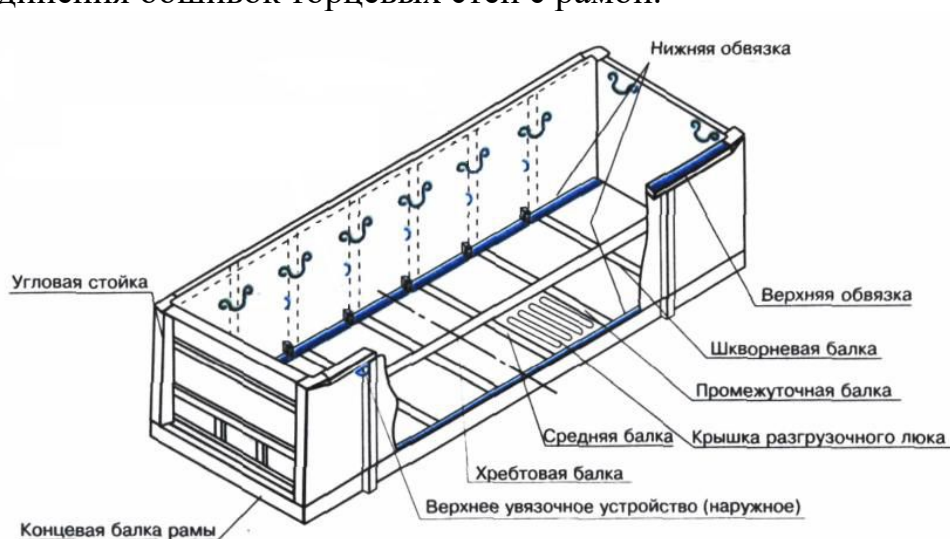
Общий вид кузова универсального полувагона с торцевыми стенами и расположение увязочных устройств.
